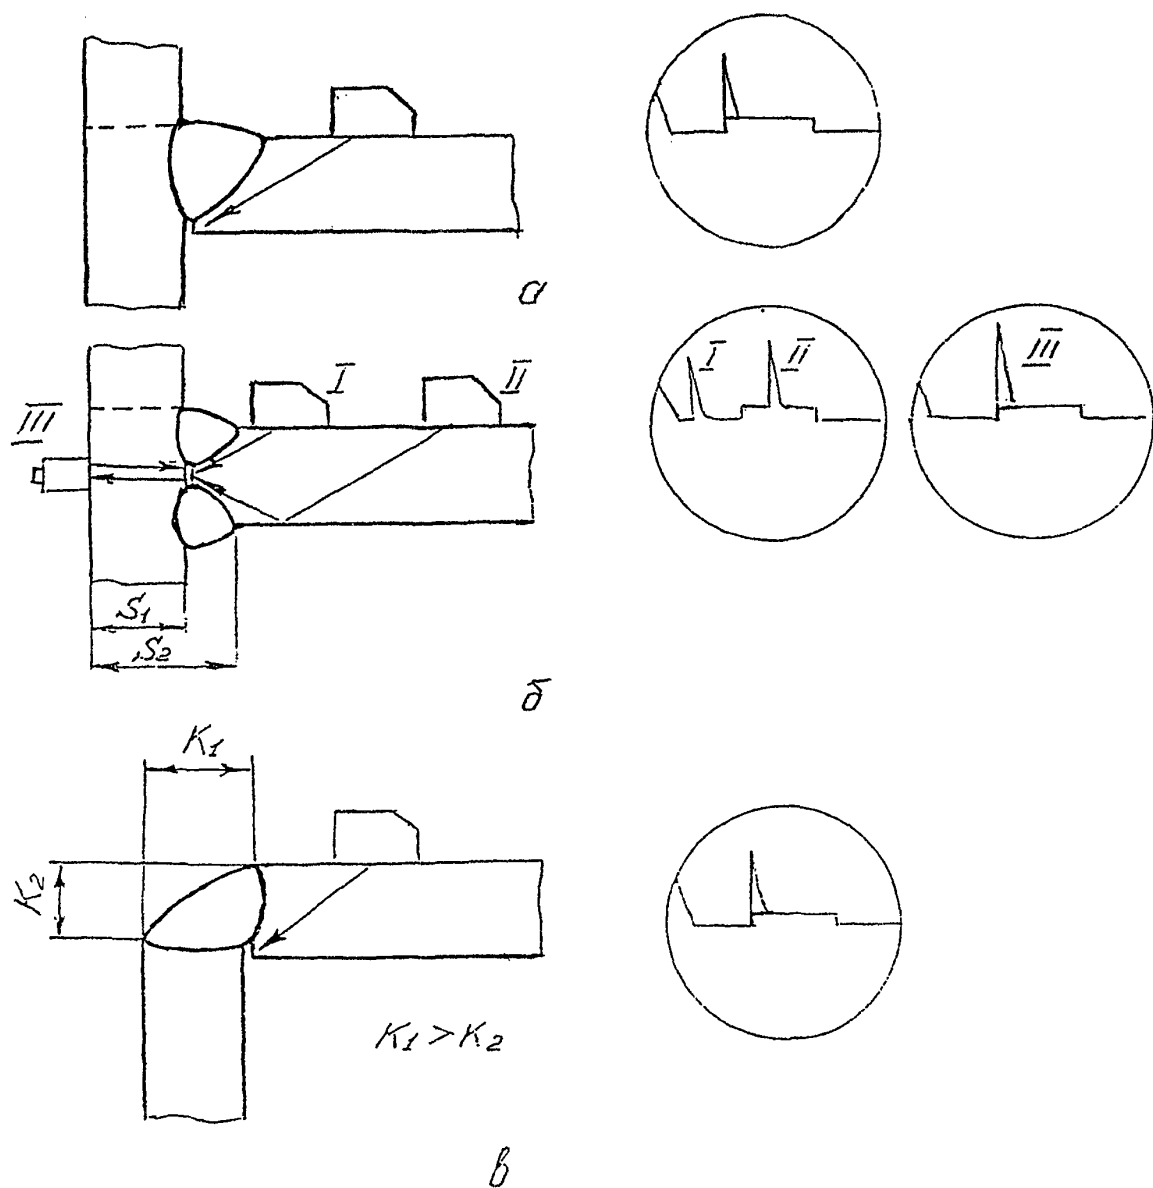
Выявление непроваров в корне швов угловых и тавровых сварных соединений, выполненных без конструктивных непроваров.
